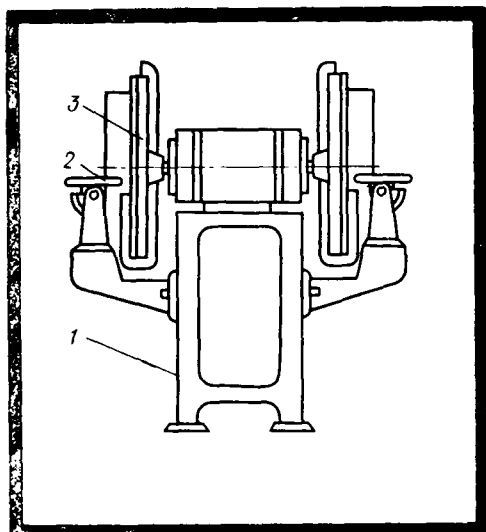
Шлифовальный дисковый станок Шл2Д-2:
